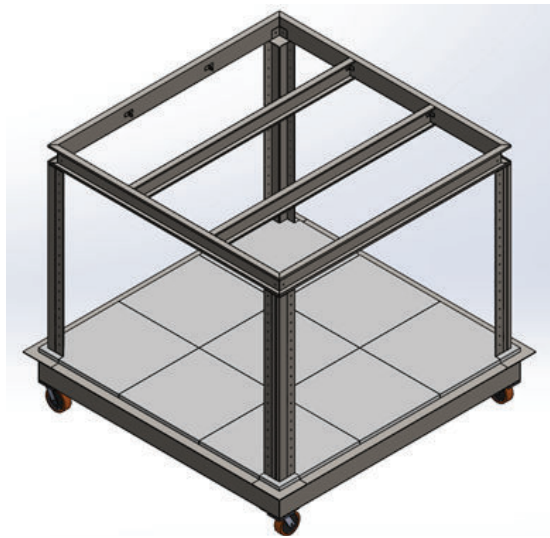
Colocación de los paneles del piso (Fuente propia)
